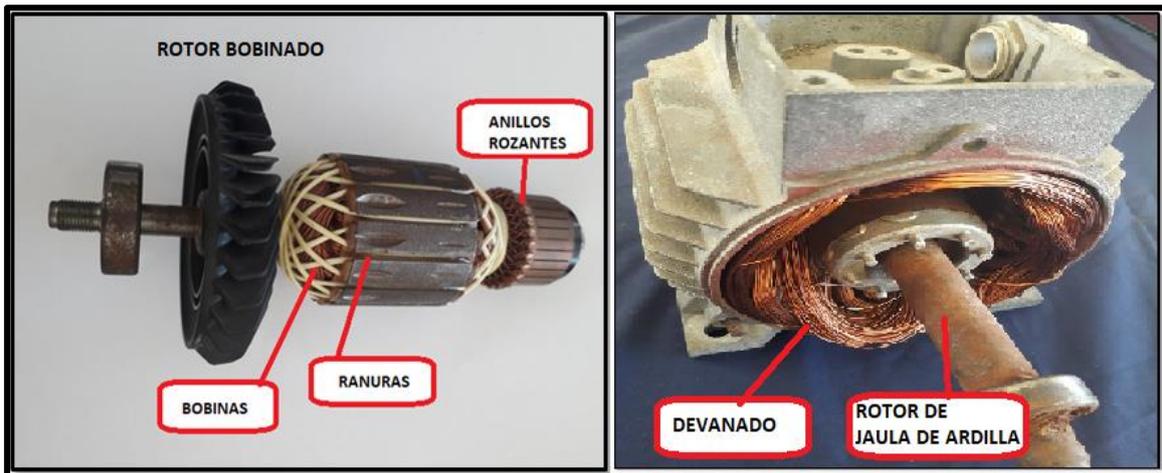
Devanado de un rotor bobinado y de un estator con rotor de jaula de ardilla. Fuente: Elaboración propia.
